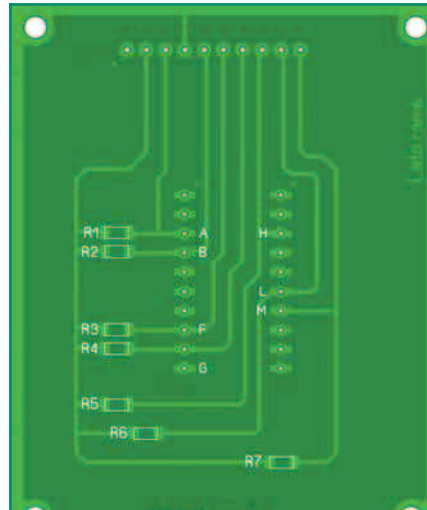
Piano di montaggio lato saldature del modulo tastierino
